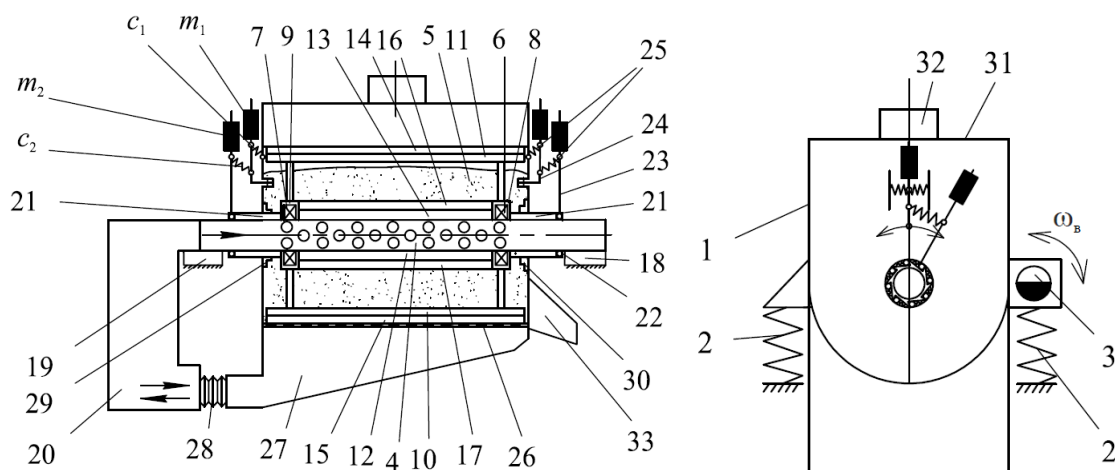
Віб्रोозонуюча сушарка з перемішувачами і маятниковими механізмами вільного ходу: 1 – камера U-подібної форми; 2 – пружини; 3 – вібророзбуджувач; 4 – газорозподільна решітка; 5 – зернова сировина; 6, 7 – корпуси підшипників; 8, 9 – підшипники; 10-13 – лопаті-перемішувачі; 14-17 – еластичні скребки; 18, 19 – опори; 20 – система подачі-відбору сушильного агента; 21 – втулка; 22 – маятникові механізми; 23, 24 – маятники; 25 – пружини; 26 – перфороване днище; 27 – дифузор; 28 – еластичне з'єднання; 29, 30 – пружні вставки; 32 – завантажувальний отвір; 33 – розвантажувальний лоток
